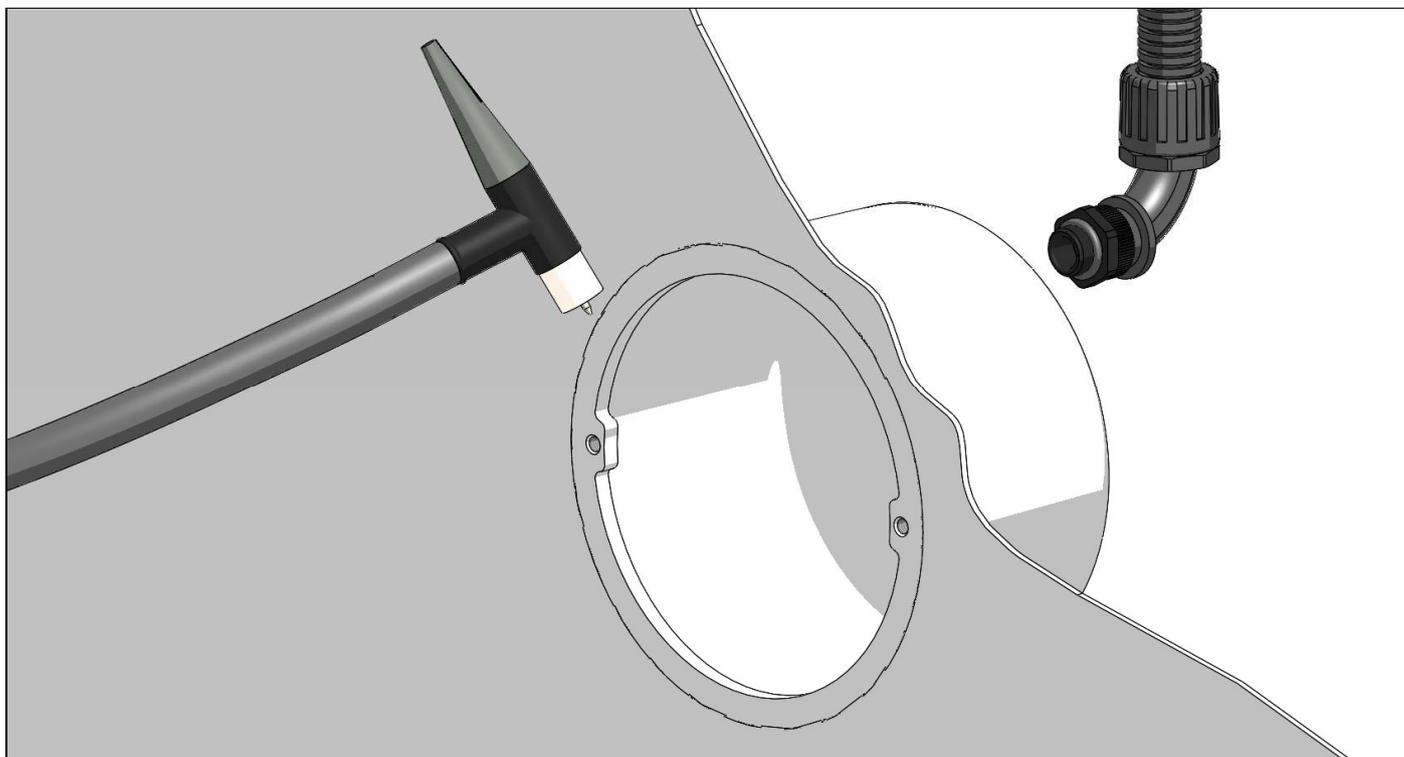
Встраиваемый корпус для бассейна из нержавеющей стали – сварка заподлицо с бассейном (затем герметично подключить систему защиты кабеля))
